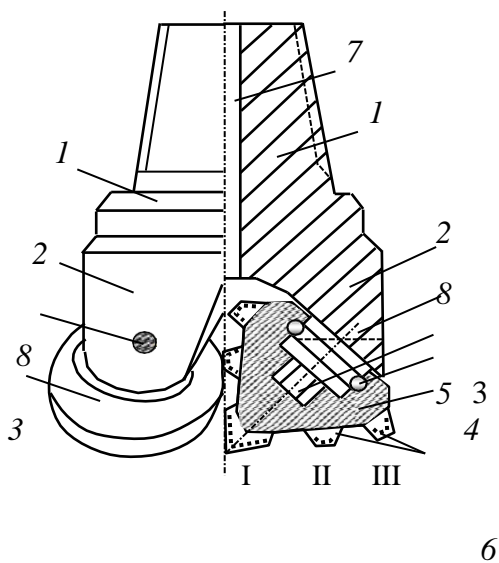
Схема трехшарошечного долота с центральным промывочным каналом, зубчатым вооружением и опорой качения на подшипниках
